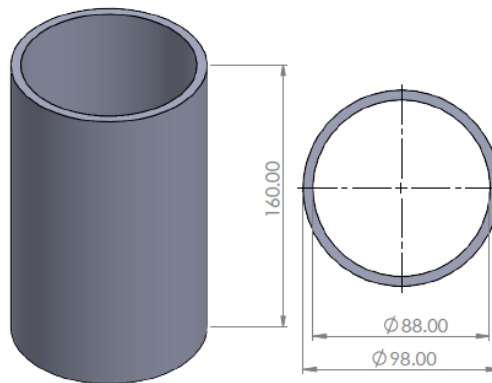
Características geométricas do dissipador cilíndrico (dimensões em mm).
